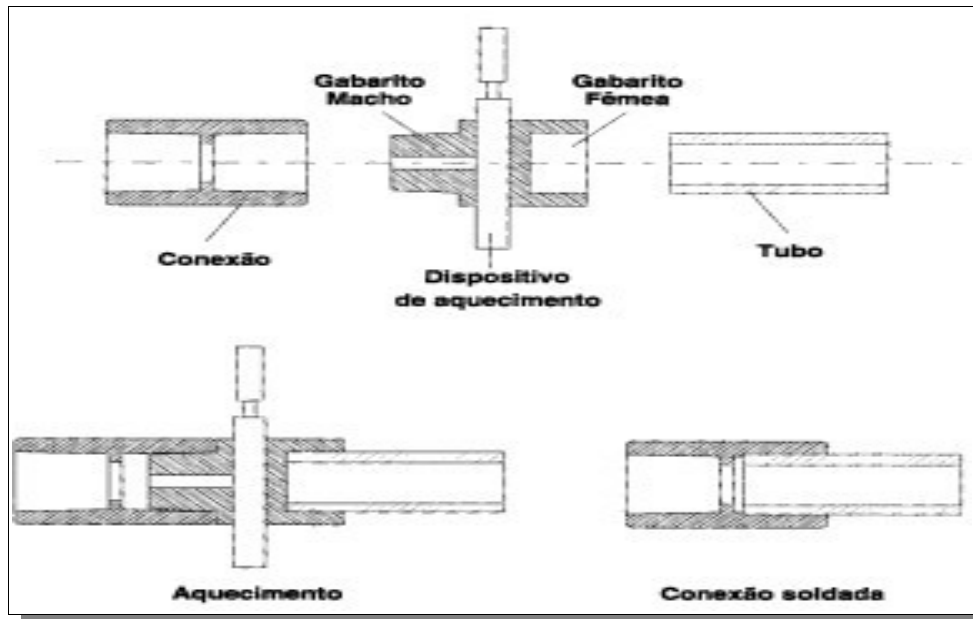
Soldagem tipo soquete ou encaixe por termofusão
